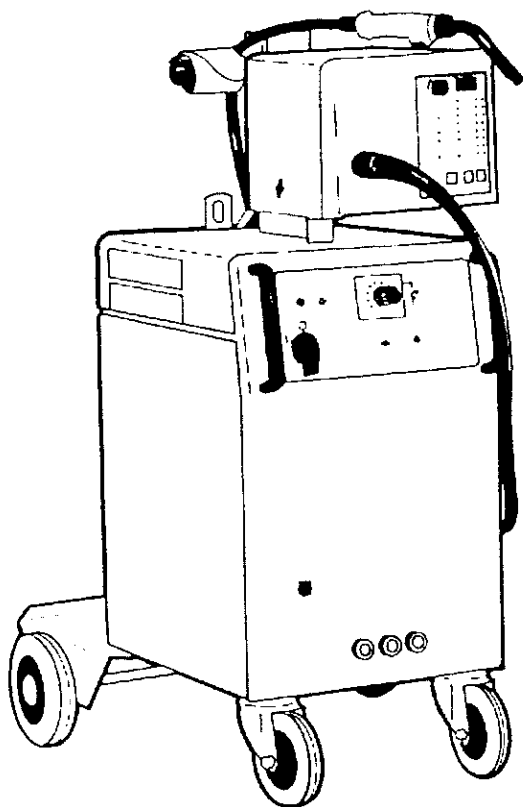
Fuente de corriente de soldadura.
